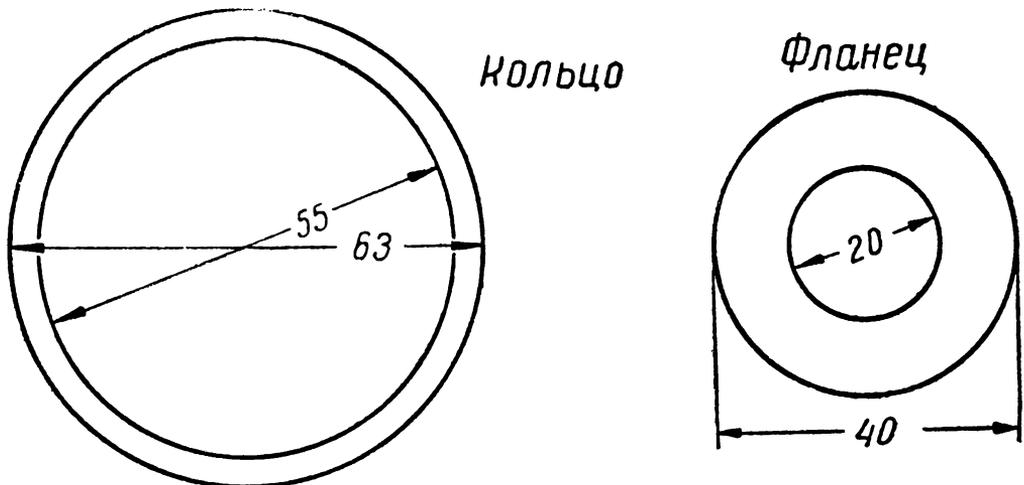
Регулировочное кольцо для трубки и фланец для рупора.
